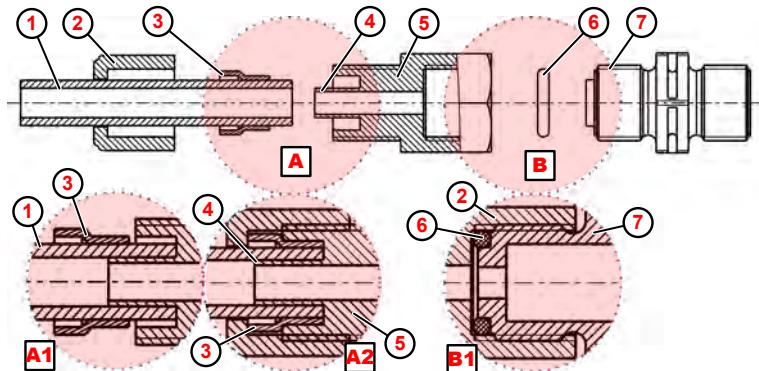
Attacco tubo rigido e tubo flessibile con manicotto di sostegno integrato.
